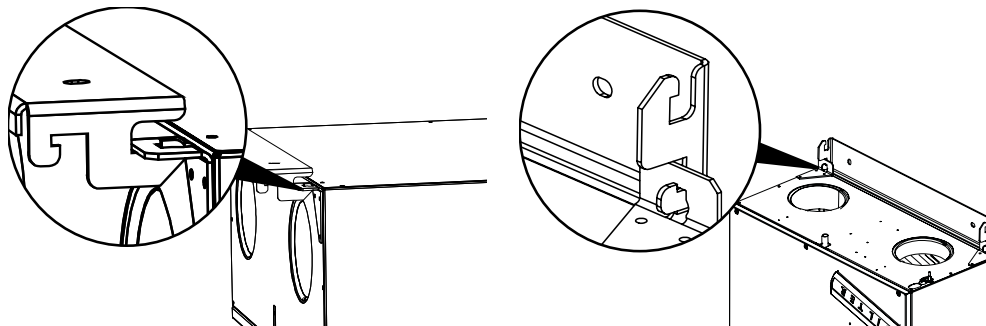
installation du support en cas de montage au plafond (à gauche) et de montage au mur (à droite)
